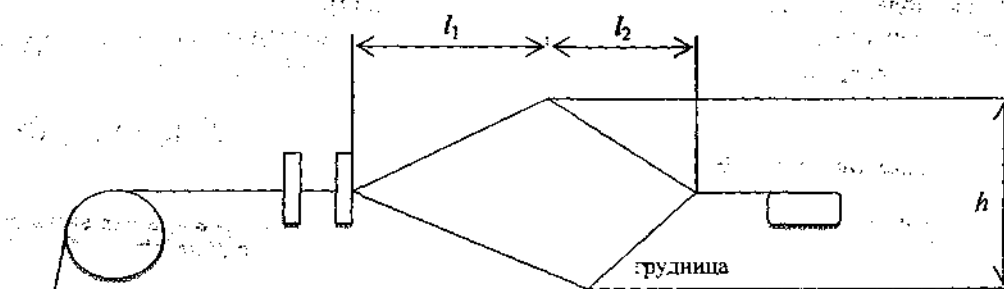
Конструктивно-заправочная схема станка СТБ2-175
